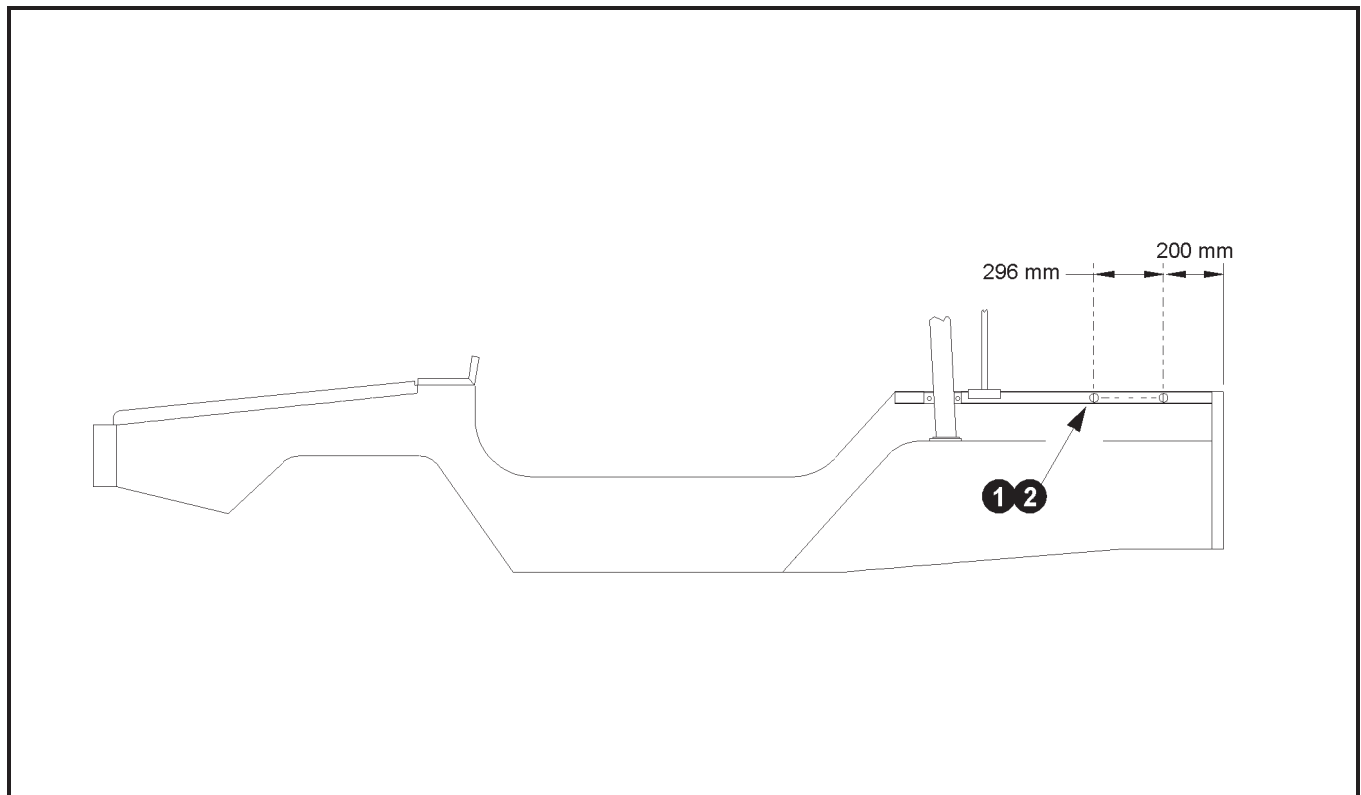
Installation des écrous-rivets aveugles à l'intérieur de la paroi arrière – CA97
